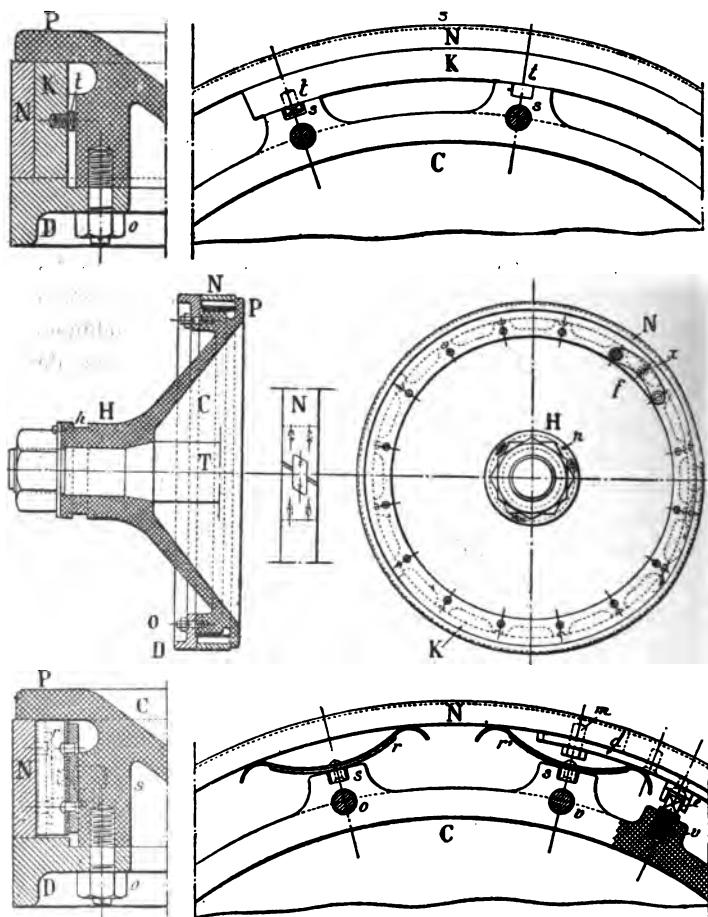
Piston en acier coulé, pour machine marine horizontale (d'après M. Demoulin). Le couvre-joint de la bague N est formé de la plaque *d*, fixée par les vis *m*; la fourche en acier *e* empêche la bague de tourner. La bague N est pressée contre le cylindre par les ressorts tels que *r*, *r'*; à la partie inférieure du piston, une cale en fonte K, maintenue par la tête des vis *t*, reporte sur la bague le poids du piston.
